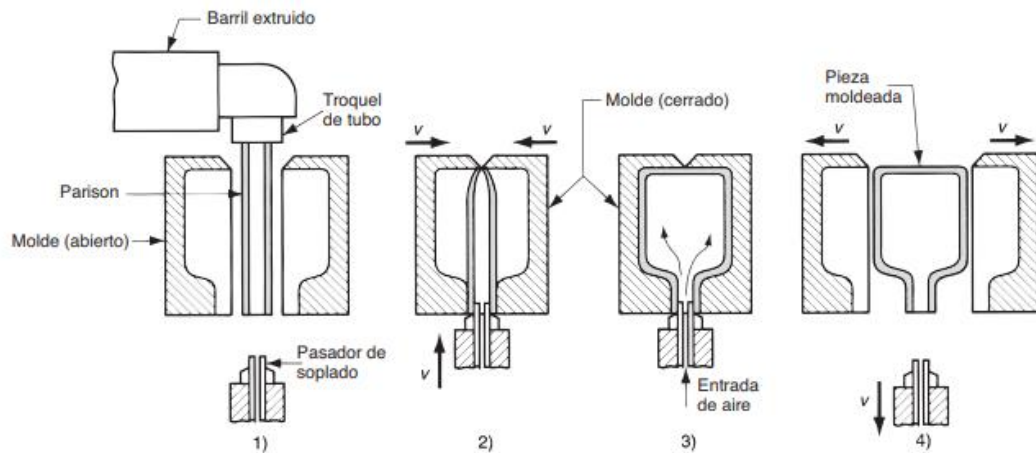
Moldeo por soplado y extrusión. Fuente: Groover, M. P. (2007). *Fundamentos de manufactura moderna: materiales, procesos y sistemas* (3ª ed., p. 289). McGraw-Hill.
